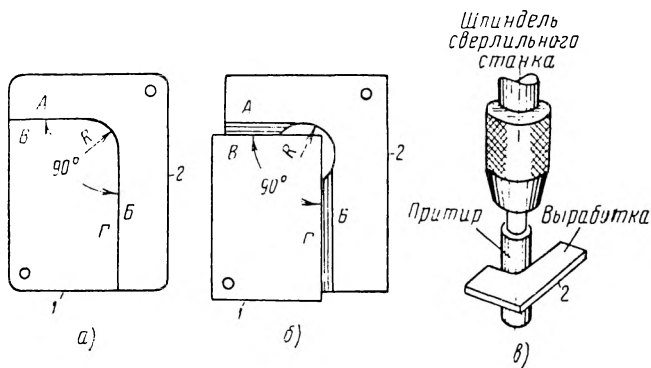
Эскиз комплекта выработок с выпуклой и вогнутой радиусными поверхностями и схема доводки выработки на сверлильном станке
